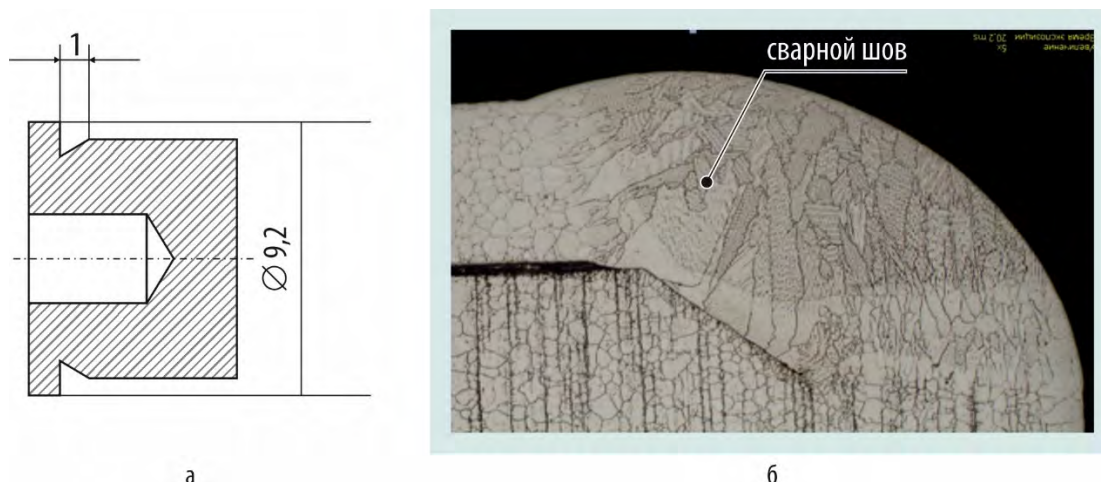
Конструкция заглушки с проточкой (а) и структура стыкозамкового сварного соединения (б), выполненного с применением заглушки с проточкой
